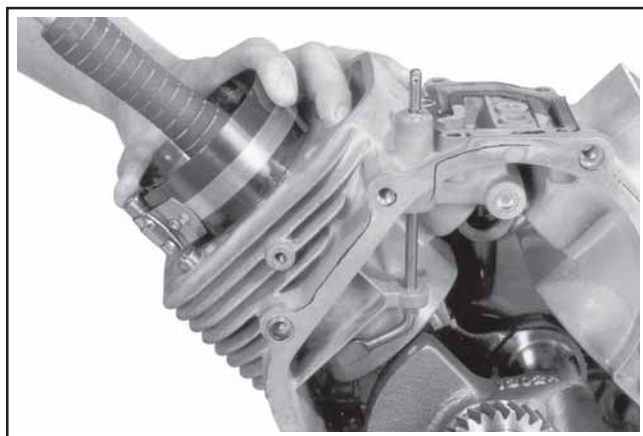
Installazione del gruppo pistone con il compressore per segmenti.
